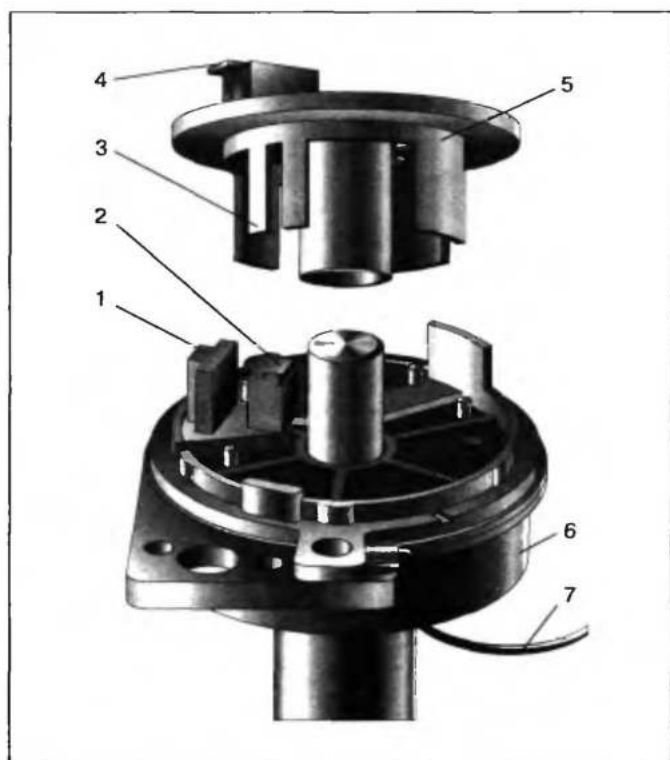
Один из вариантов конструкции распределителя зажигания с датчиком частоты вращения/положения распределительного вала (4- цилиндровый двигатель):
